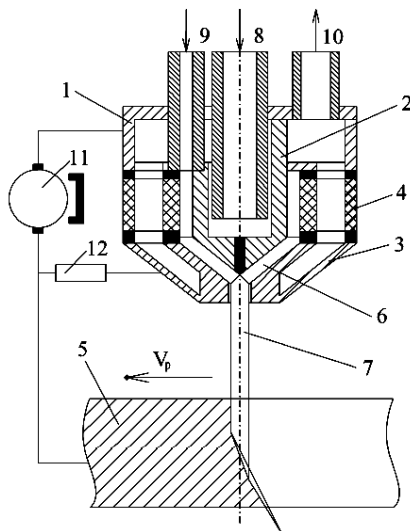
Режущий плазмотрон: 1 – корпус; 2 – электрод (катод); 3 – формирующий наконечник; 4 – изолятор; 5 – разрезаемый металл; 6 – дуговая камера; 7 – столб дуги; 8 – подача охлаждающей воды; 9 – подача плазмообразующего газа; 10 – слив воды; 11 – источник тока; 12 – устройство зажигания дуги
